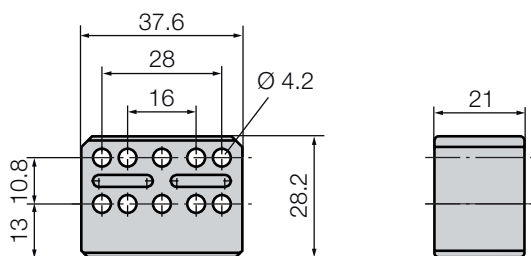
Medidas de montaje del sensor de posición BTL6-A-3800-2
